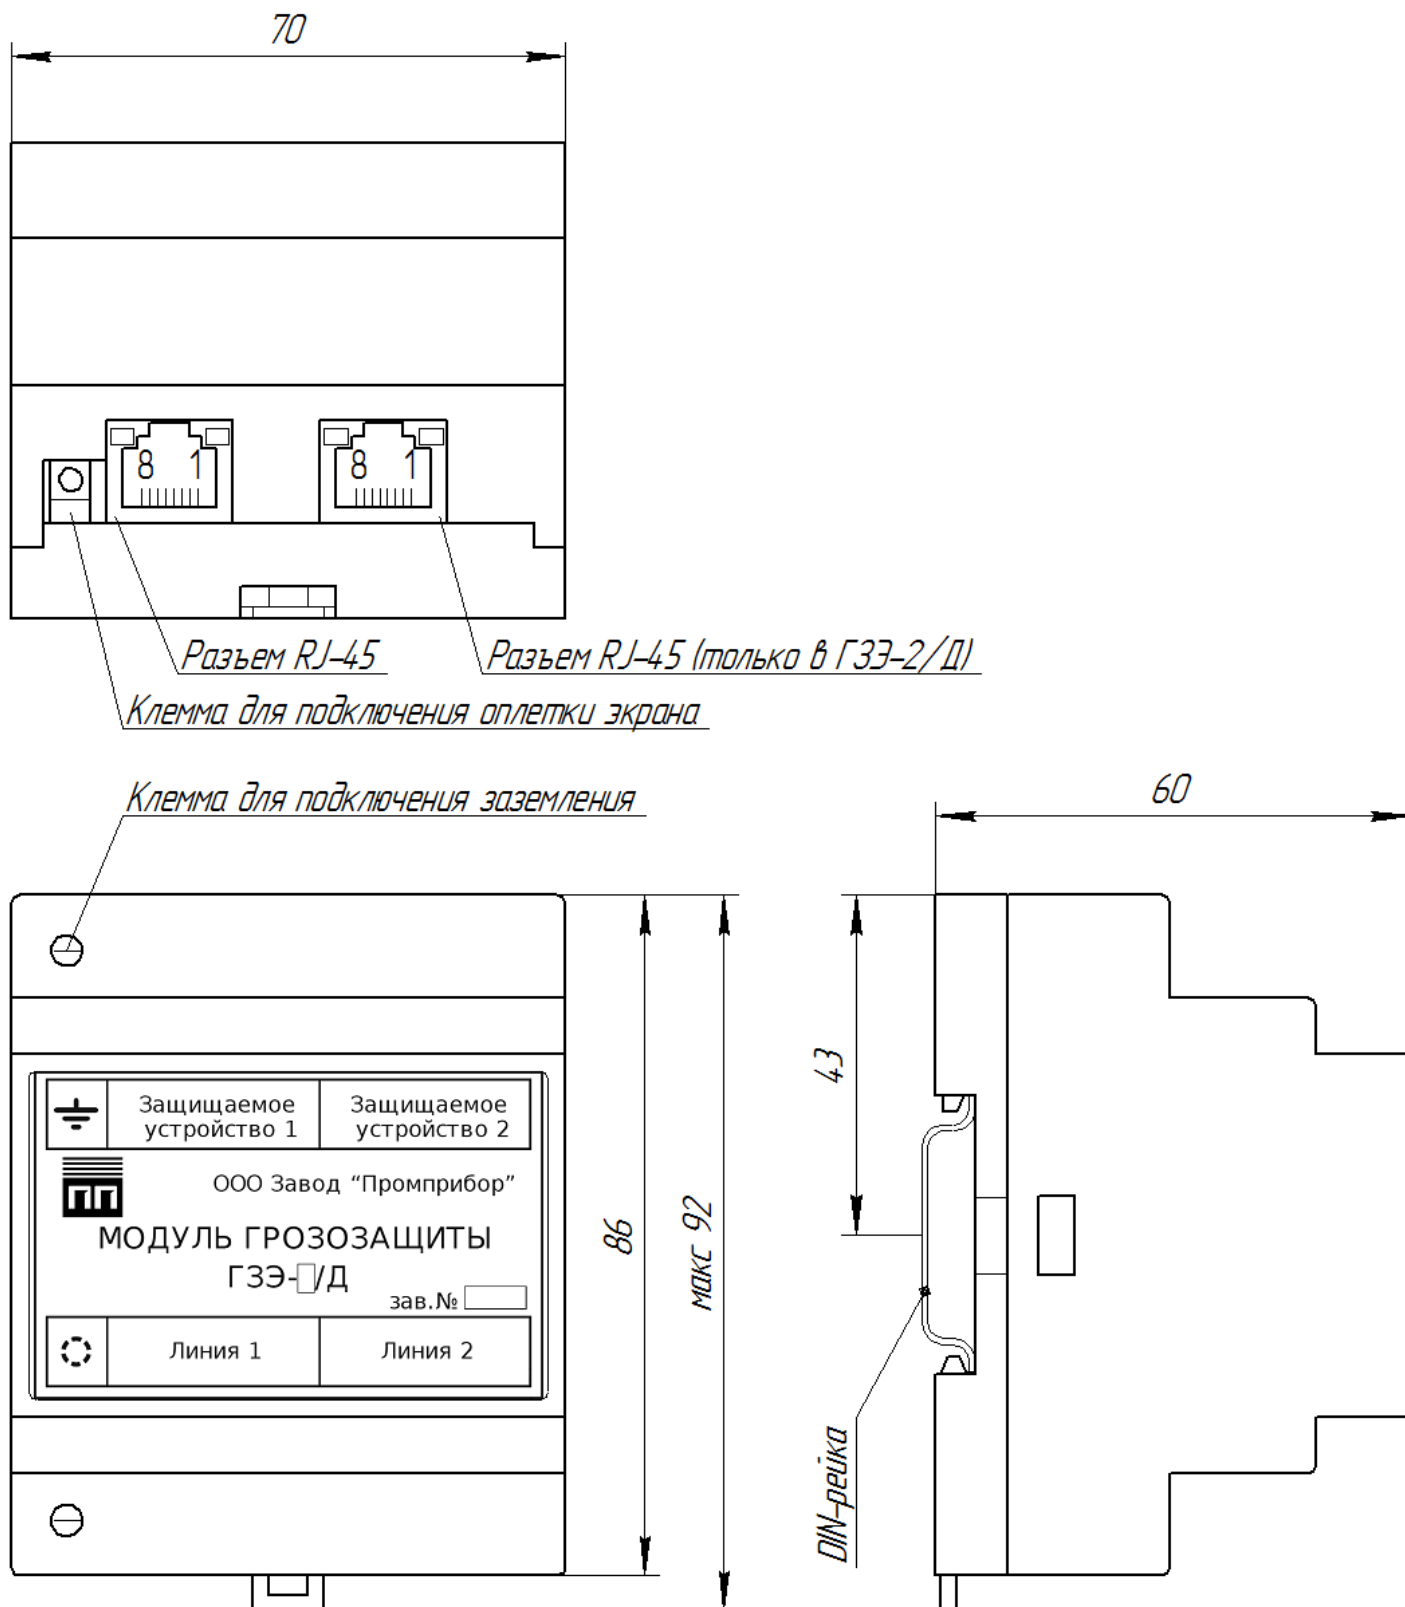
Габаритные и установочные размеры модуля грозозащиты
